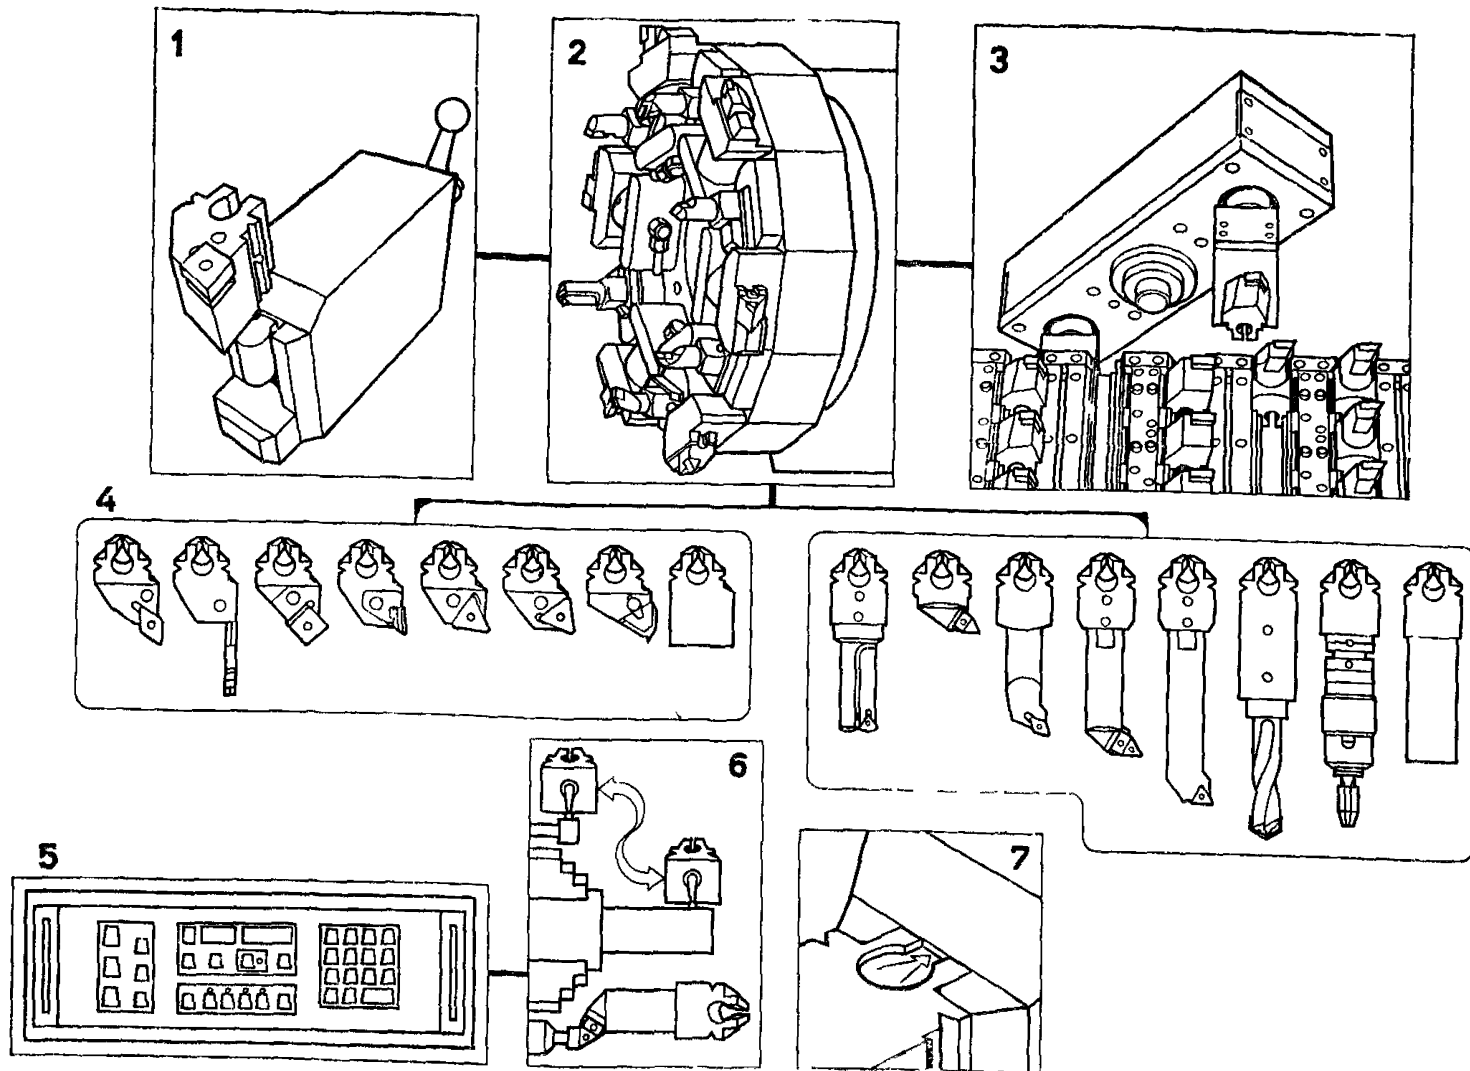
Пример установления стандартных присоединительных поверхностей обеспечивающих единство блочно модульного метода агрегатирования в ЦКИ для станков токарной группы
